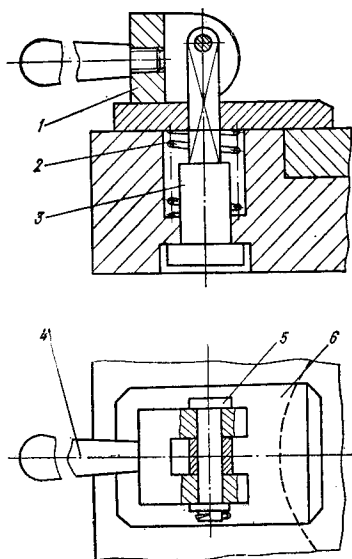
Кулачковый механизм разъемной пресс-формы.
